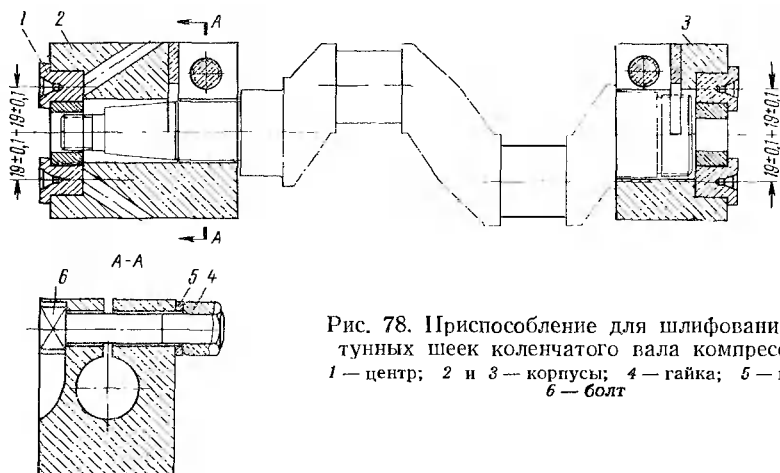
Приспособление для шлифования шатунных шеек коленчатого вала компрессора:
